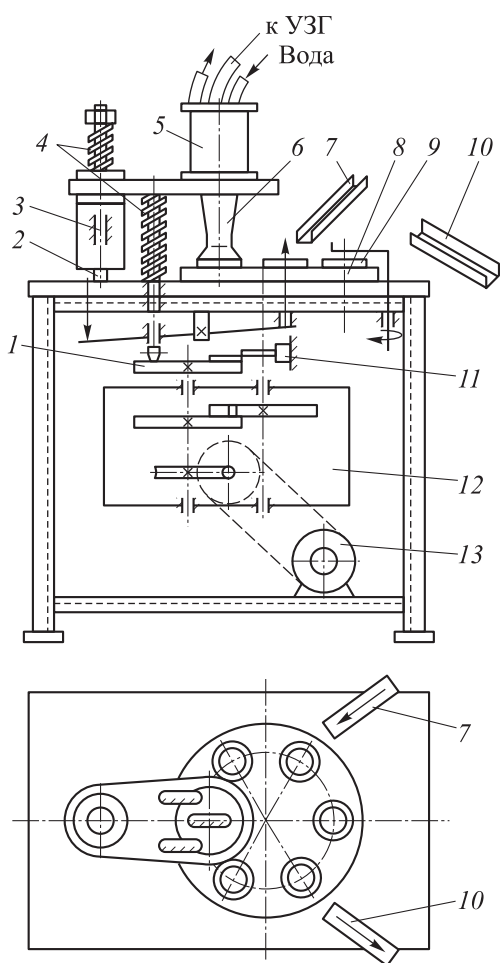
Схема работы ультразвуковой сварочной установки УПК-15М1
